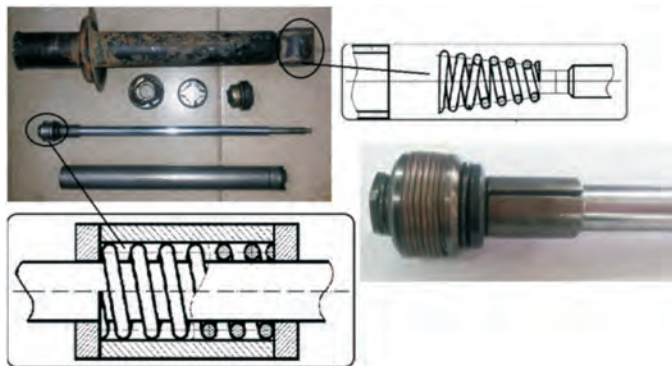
Задний амортизатор автомобиля ВАЗ 2108: конструкция поршня с уплотнением из винтовой цилиндрической пружины квадратного сечения с поджатыми витками
